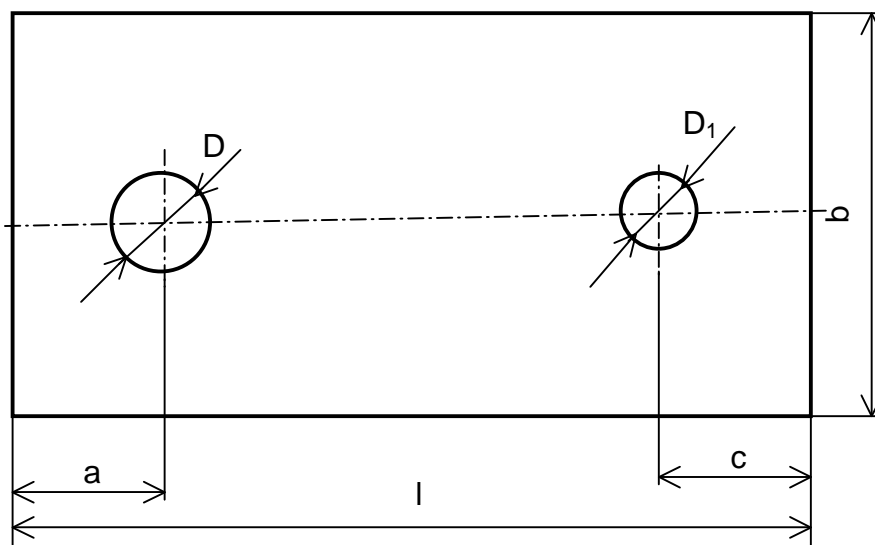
Образец из углепластика для испытаний на смятие согласно [15]
